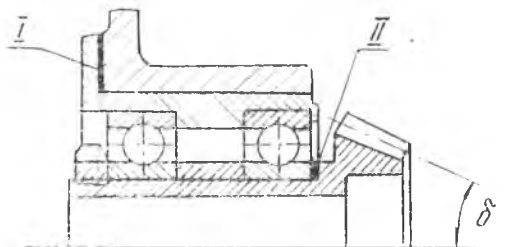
Примеры расположения компенсаторов для обеспечения бокового зазора в зацеплении конических зубчатых колес
